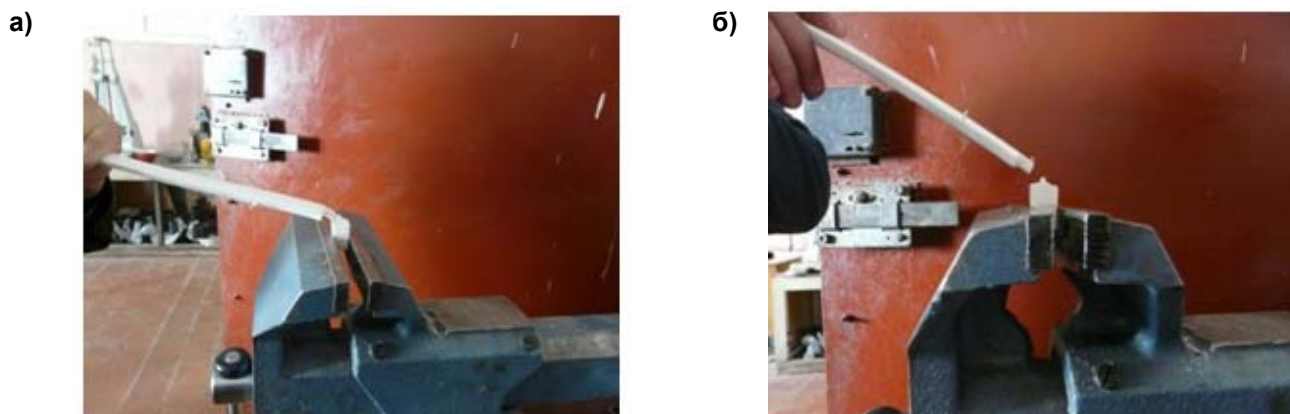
Общий вид испытаний на отдр образцов сварных соединений: а) изгиб свободной части образца; б) характерное разрушение по основному материалу
